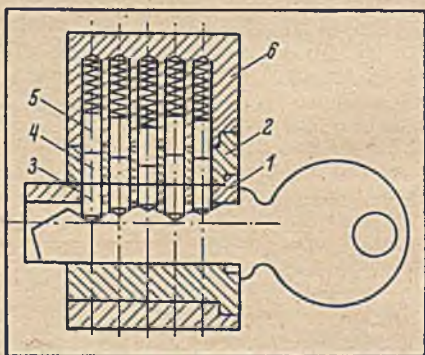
Schließzylinder mit ineinandergelagerten Innenzylindern
